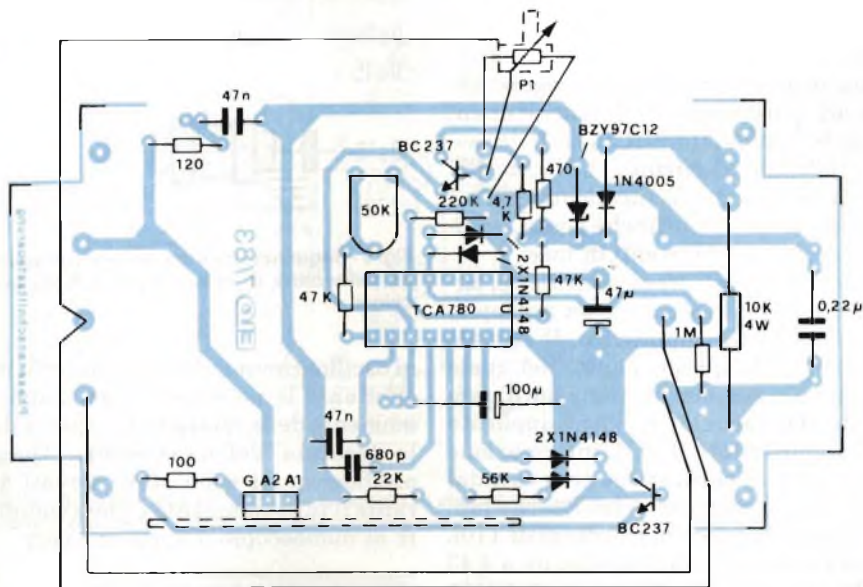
Disposizione dei componenti sul circuito stampato.
